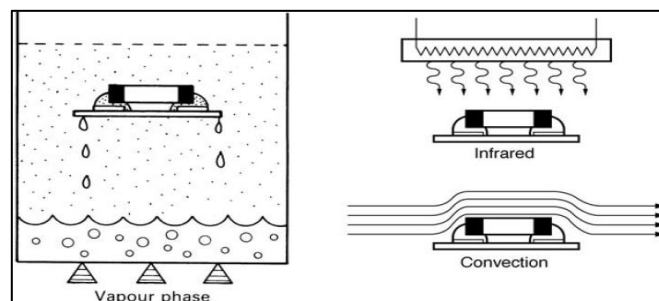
Opciones de soldadura por reflujo
